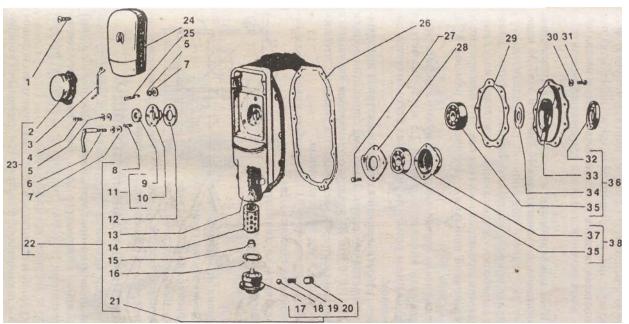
Детали ісаріера двигателя мотоцикла "Урал" М66 и М67-36: І - винт М6х22 крепления крышки (2 шт.); 2 - прерьмаіе ів в сборе; 3 - провод; 4 - винт М5х16 (2 шг.); 5 - шайба 5Л (5 шт.); 6 -держатель крышки прерывателя с планкой; 7 - шайба 5 (2 шт.); 8 - винт М5х16 (4 LUI.); 9 - сальник распредвала в сборе; 10 - обойма сальника; \\ - обойма с сальником; 12 - прокладка обоймы сальника; 13 - крышка распределительной коробки; 14 - элемент фильтрующий; 15 - втулка фильгрующего элемента; 16- кольцо уплотнительное; 17 - пробка масляного фильтра; 18 - шарик 10 мм; 19 - пружина клапана; 20 - вин г установочный; 21 - пробка в сборе; 22 - крышка распределительной коробки в сборе; 23 - крышка распределительной коробки с прерывателем в сборе; 24 - крышка передняя; 25 - винт М5\22 (2 шт.); 26 - прокладка (2 шт.); 27 - болт М6х16 (9 цп.); 28 - крышка корпуса переднего подшипника с трубкой; 29 - прокладка корпуса заднего подшипника; 30 - шайба 6 (9 шт.); 31 - болт М6х16 (9 шт.); 32 - манжеты с пружиной; 33 - корпус подшипника задний; 34 - маслоотражатель; 35 - подшипник (2 шт.); 36 - корпус подшипника в сборе; 37- корпус подшипника передний; 38 - корпус подшипника передний в сборе
